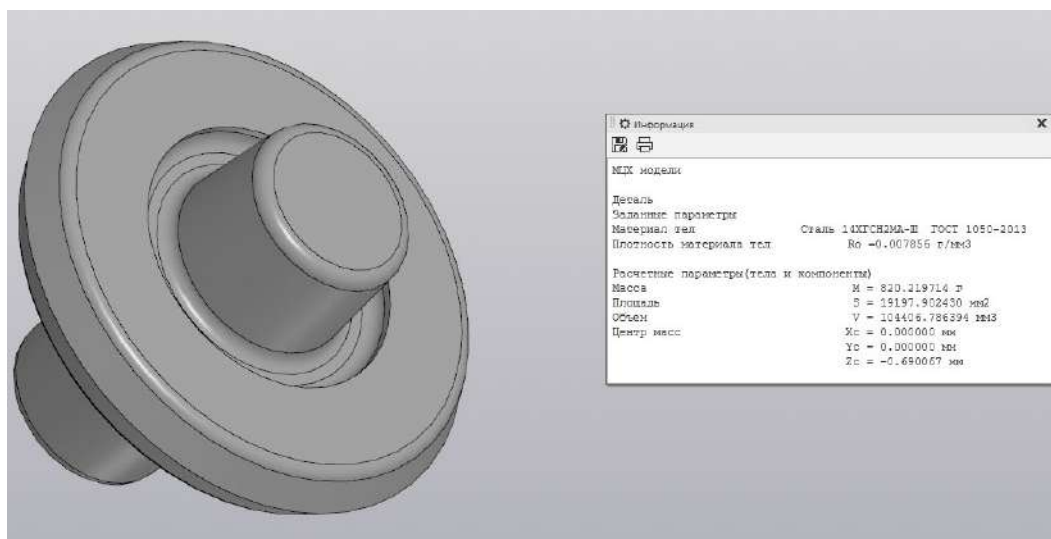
Тривимірна модель заготовки, що отримана штамповкою на КГШП
